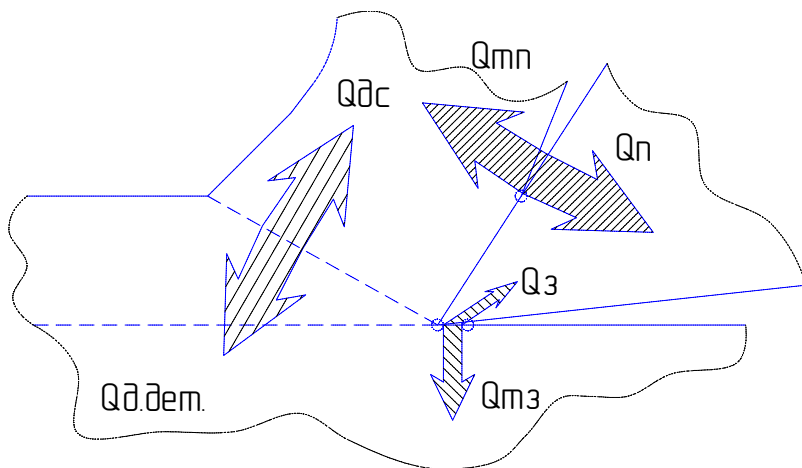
Потоки тепла в стружку, інструмент та деталь
